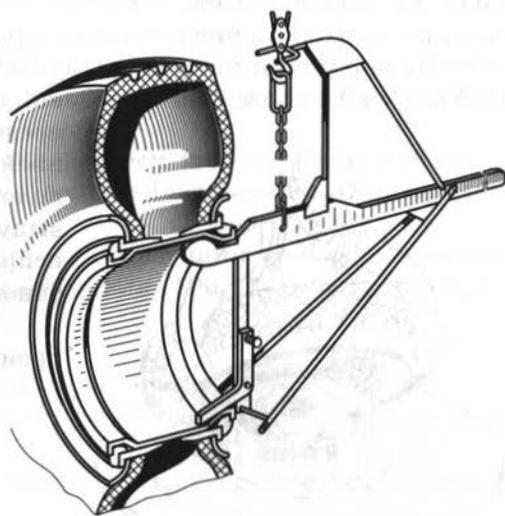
Приспособление на базе автопогрузчика для снятия сверхкрупногабаритных колес карьерных самосвалов:
